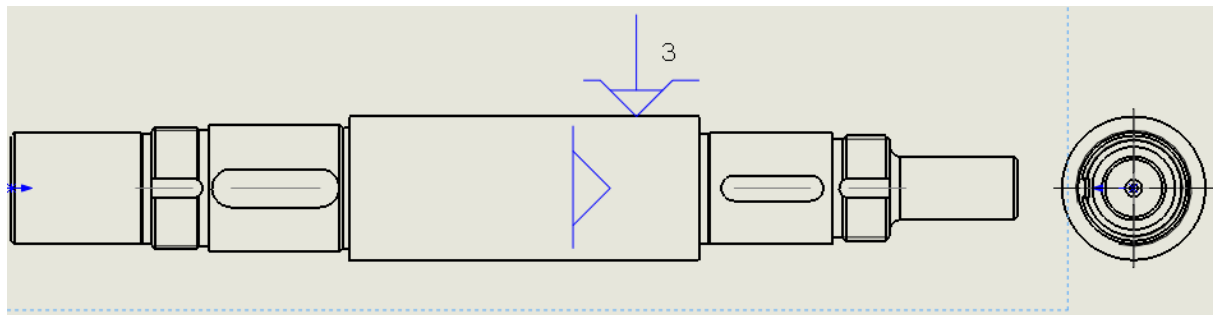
Теоретична схема базування для обробки поверхонь 10-15
